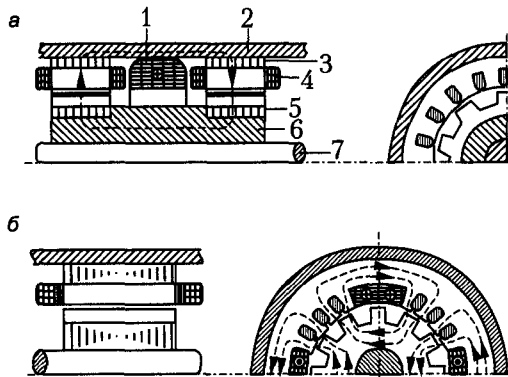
Устройство индукторного генератора: а — одноименнополюсного; б — разноименнополюсного; 1 — катушка возбуждения; 2 — корпус; 3 — пакет статора; 4 — обмотка переменного тока; 5 — пакет ротора; 6 — втулка ротора; 7 — вал
